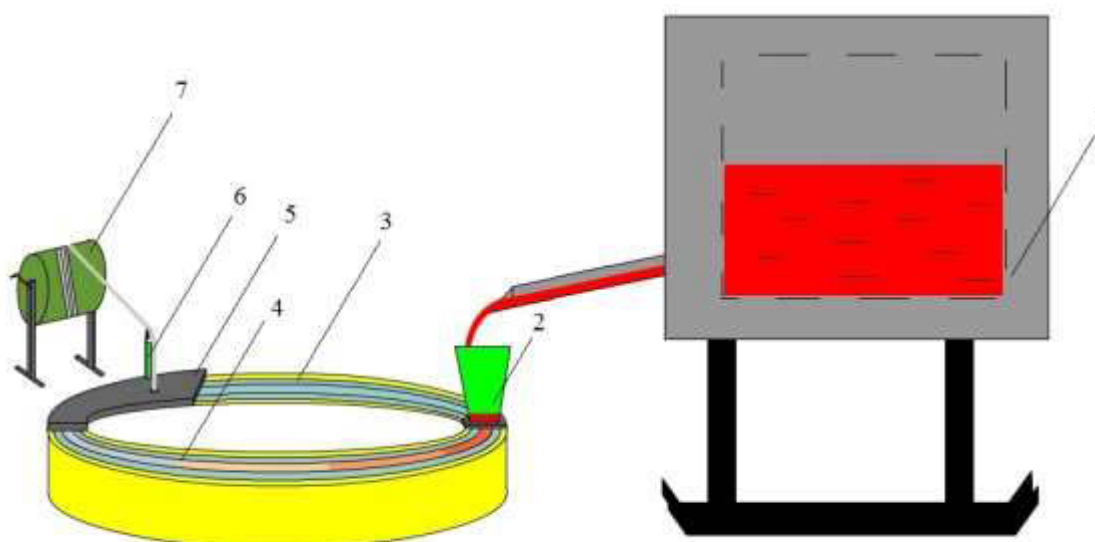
Общий вид схемы совмещенного литья и прессования цветных металлов:
